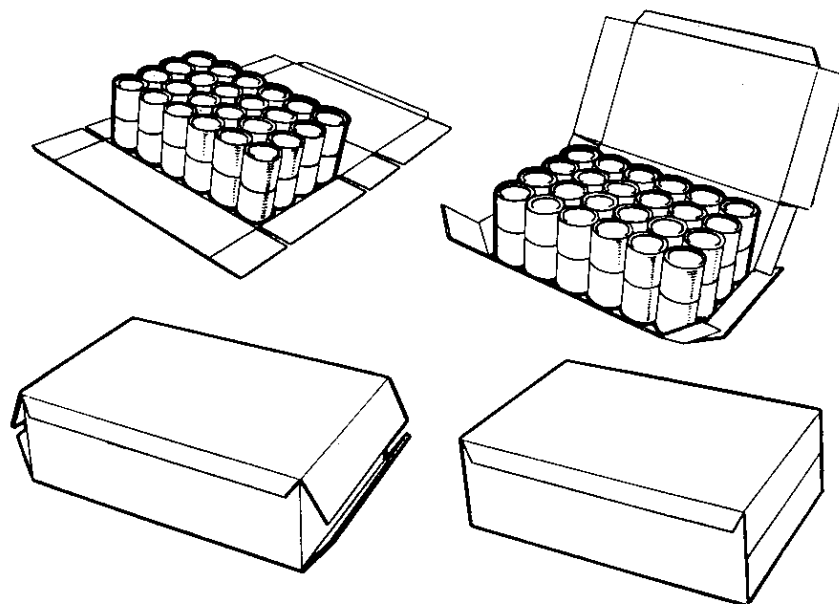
Упаковка консервных банок по способу оборачивания заготовки вокруг пакета изделий
